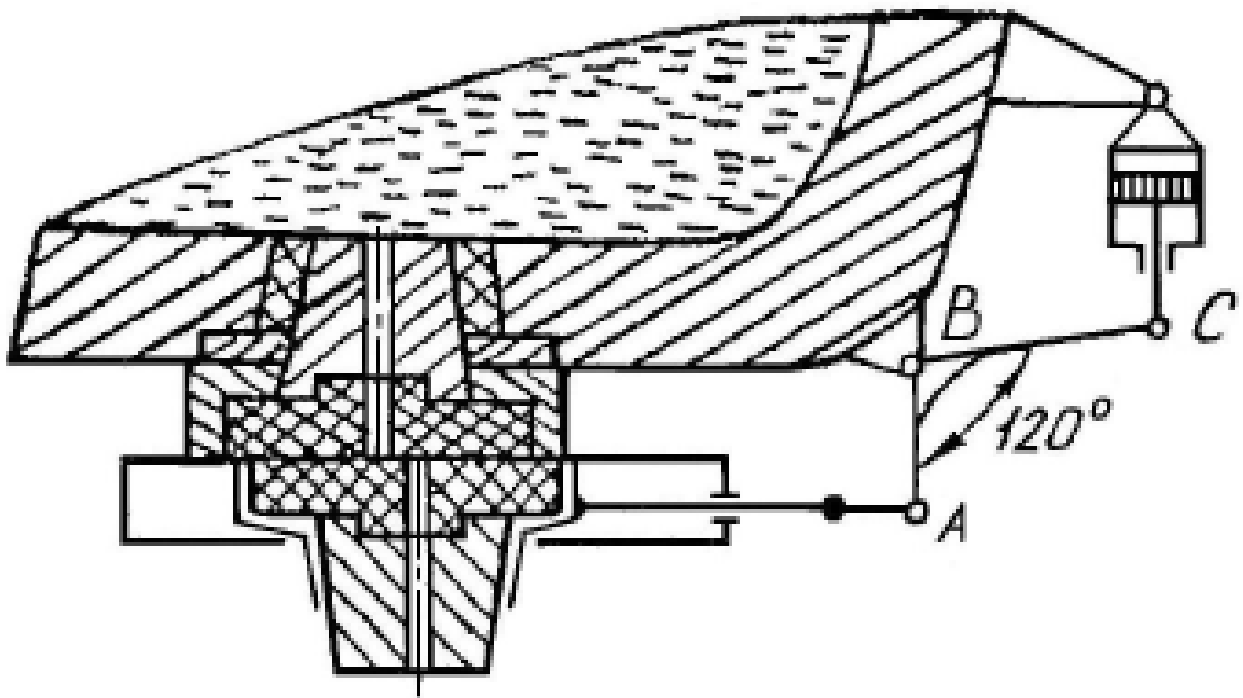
Схема шибера затвора сталеразливочного ковша
